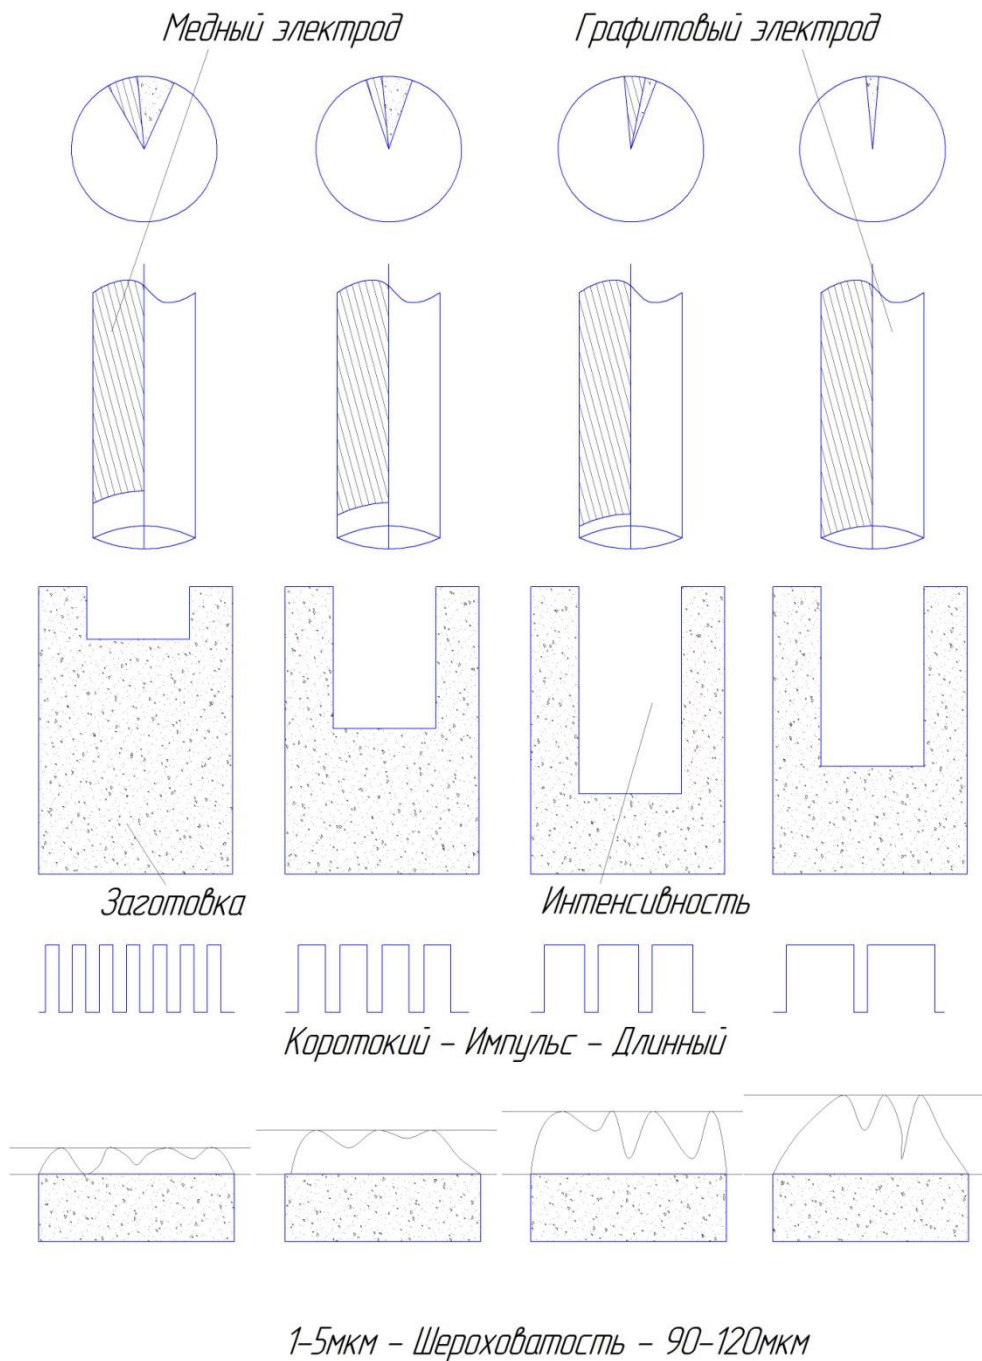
Соотношение шероховатости обрабатываемых поверхностей и зазора энергии разряда
